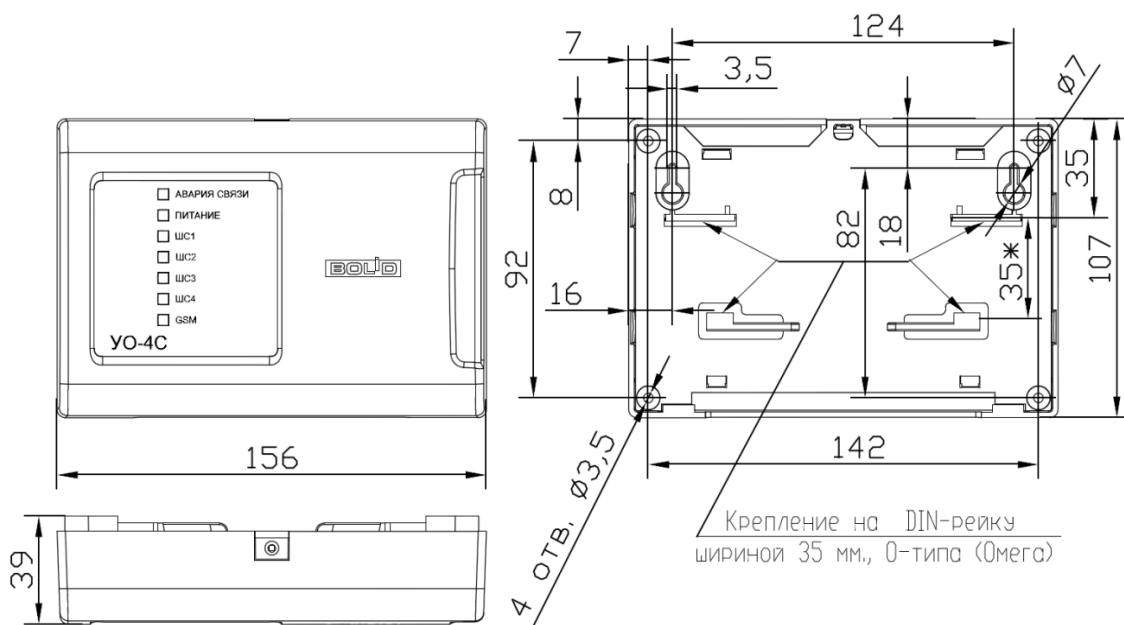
Габаритные и установочные размеры корпуса ПОО УО-4С
